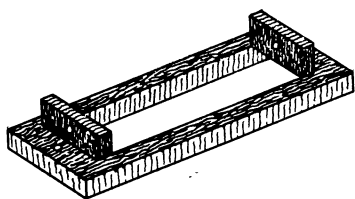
Рамка крепления звукоснимателя к корпусу гитары.
